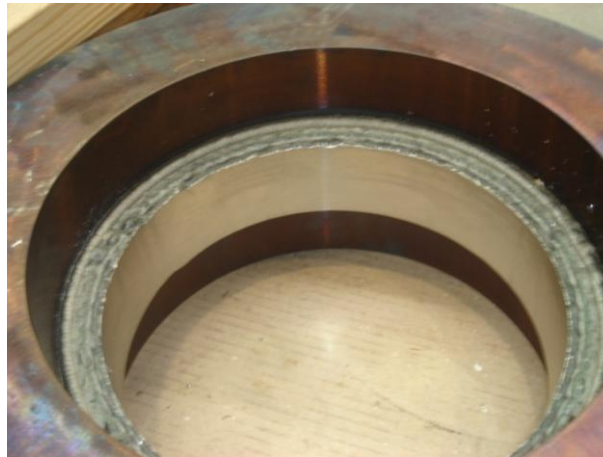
Detalhe da usinagem realizada para nivelar a 10ª camada depositada.
